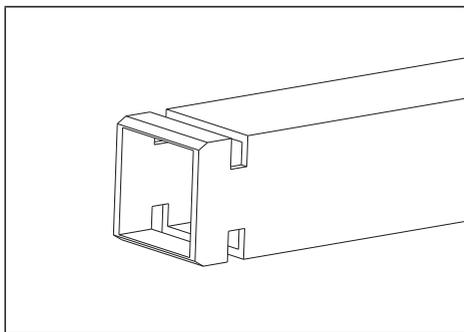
Scanalature sul supporto trasversale Multi Wall
